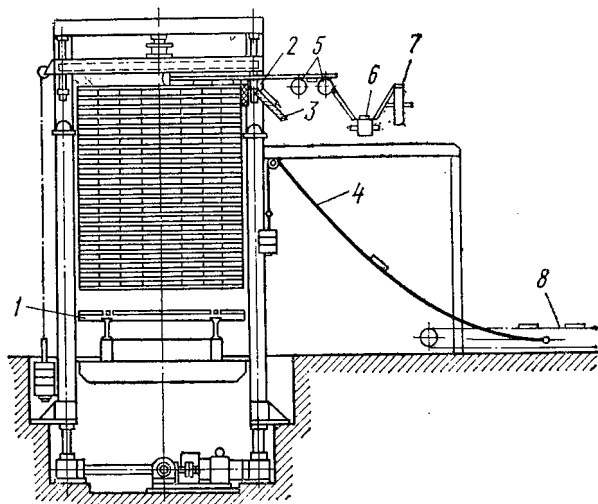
Вертикальный подъемник с приспособлением для разборки штабелей (МЛТИ):
